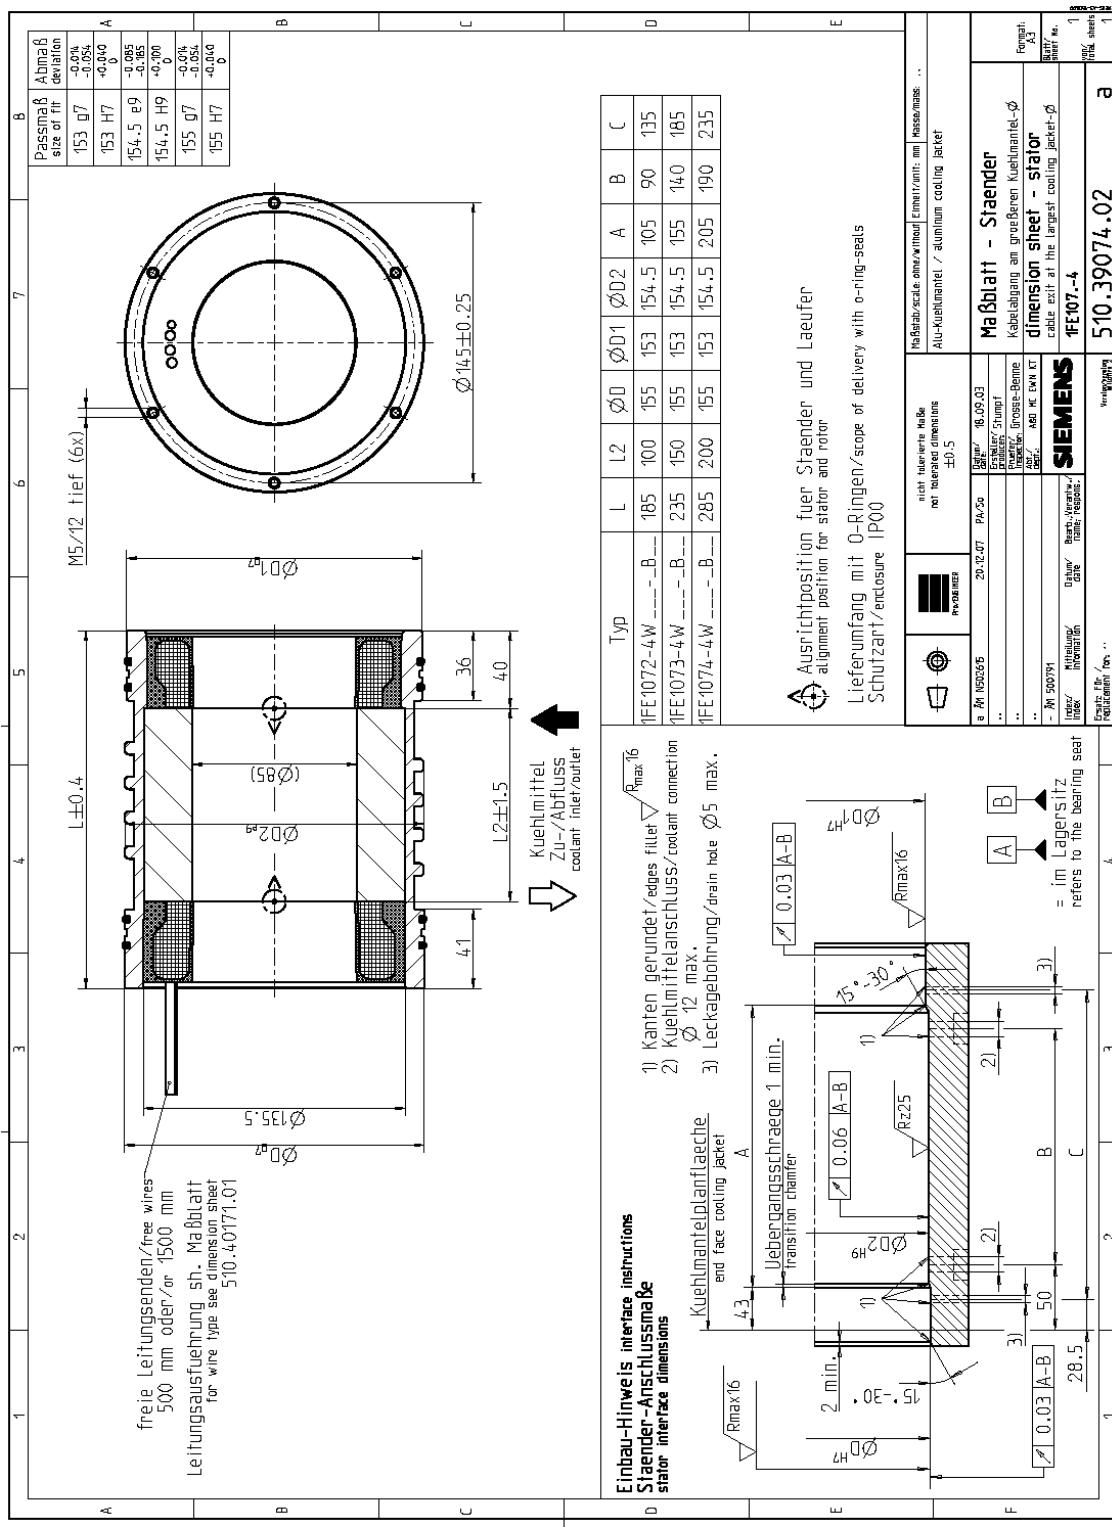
1FE107□-4, Ständer mit Kühlmantel, Kabelabgang am größeren Kühlmanteldurchmesser
